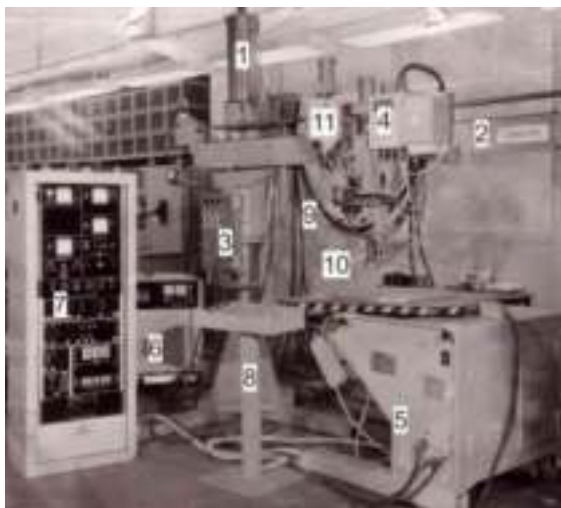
Установка плазмово-наплавлювальна.
